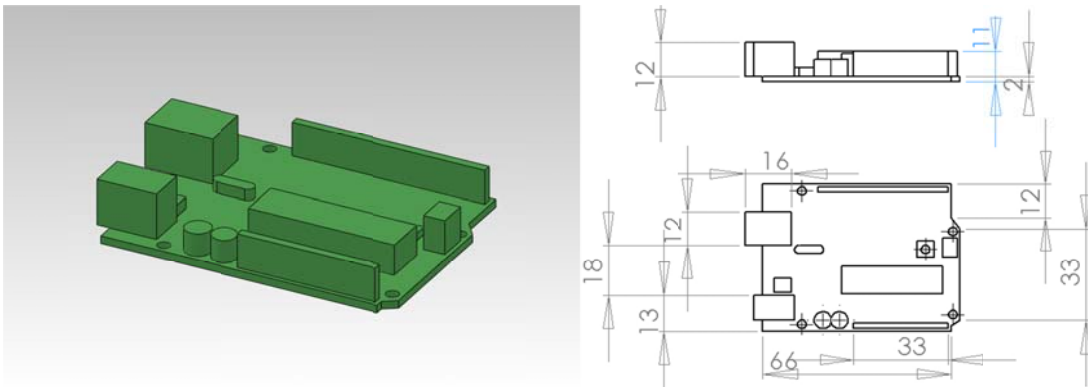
Dibujo CAD de la tarjeta Arduino uno.
